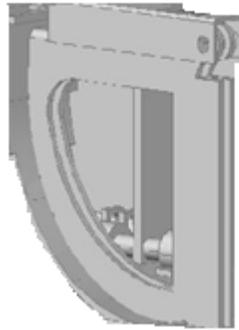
Diseño Mecánico de Maquina empaquetadora
